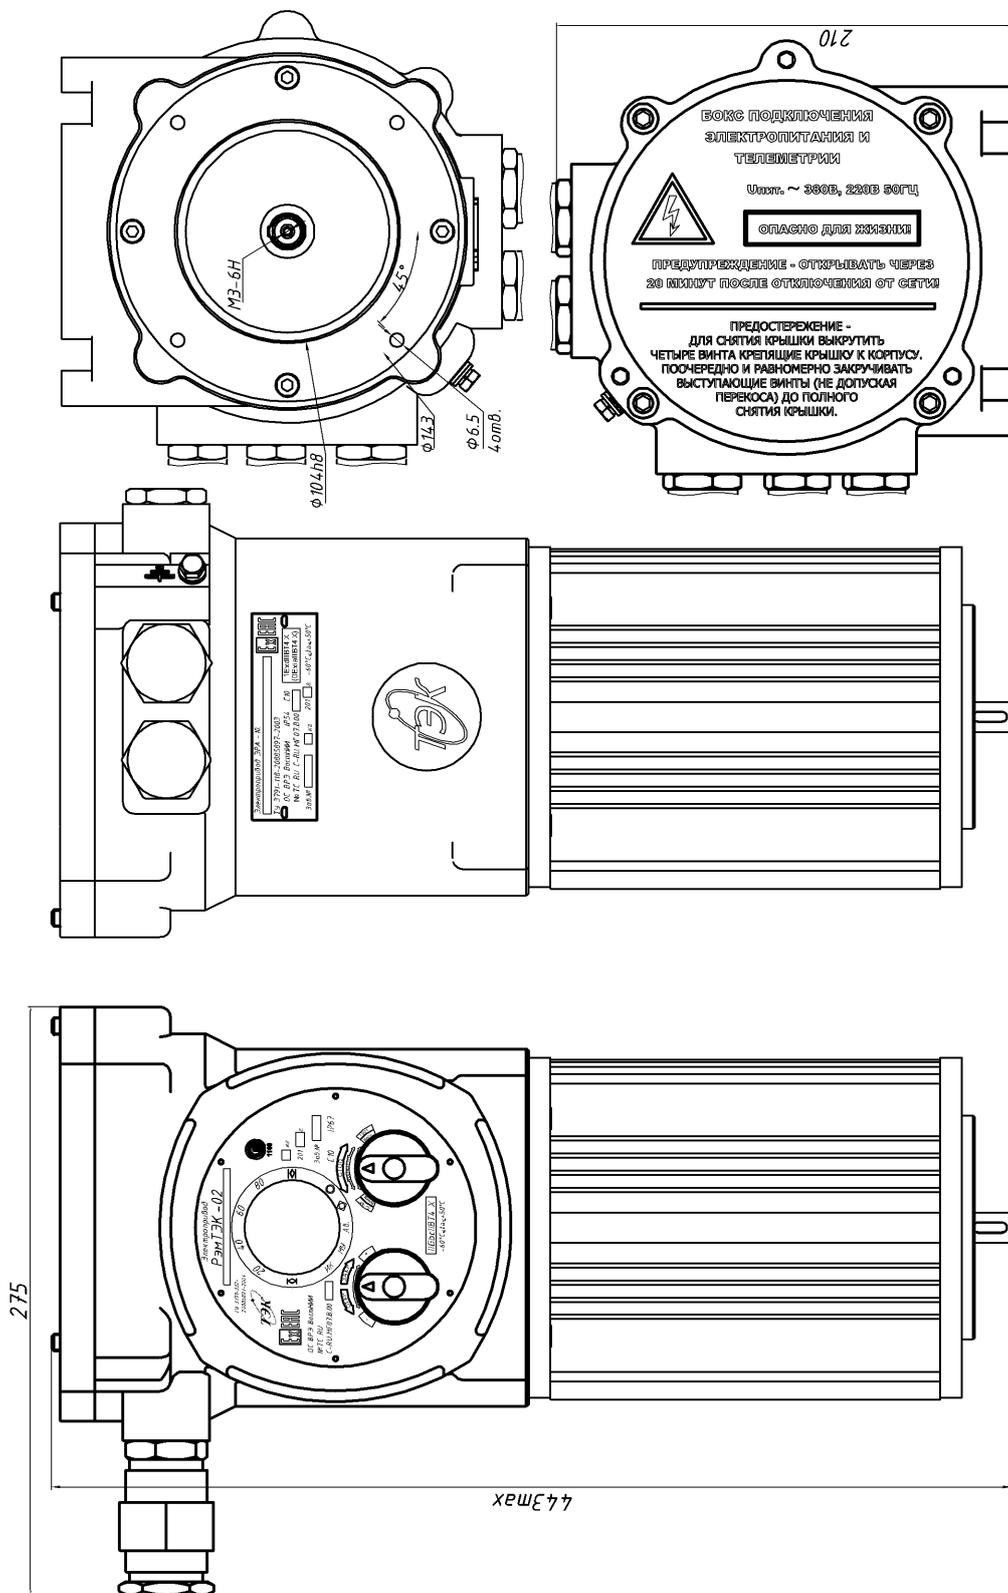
Внешний вид и габаритные размеры ЭРА-10 конструктивного исполнения "8"
